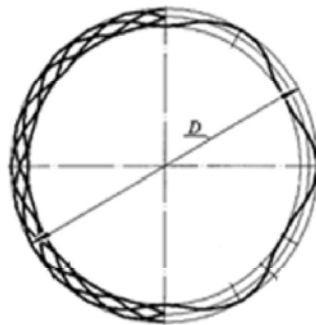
Поперечный разрез заготовки после обработки поверхности вибронакатыванием со статико-импульсным нагружением
